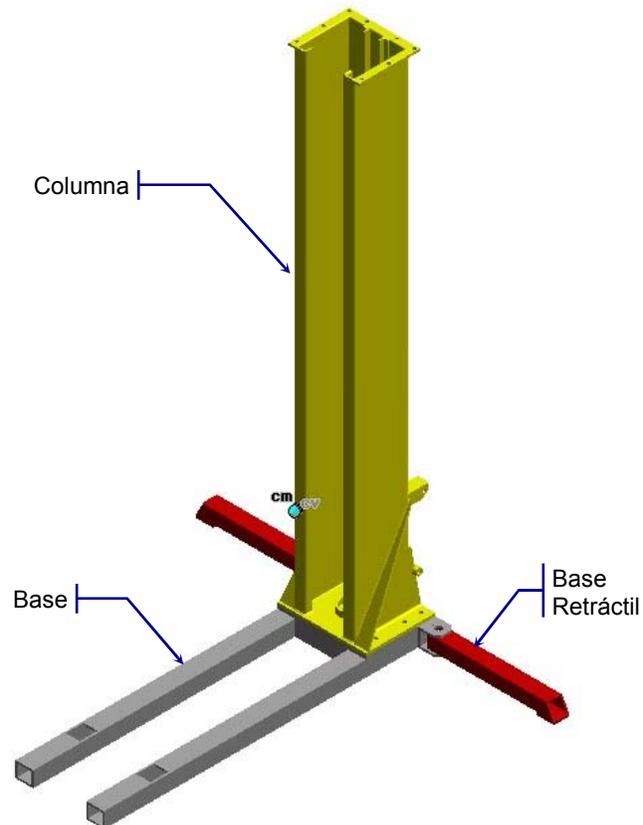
Vista 3D del Conjunto Columna Base de Soporte
